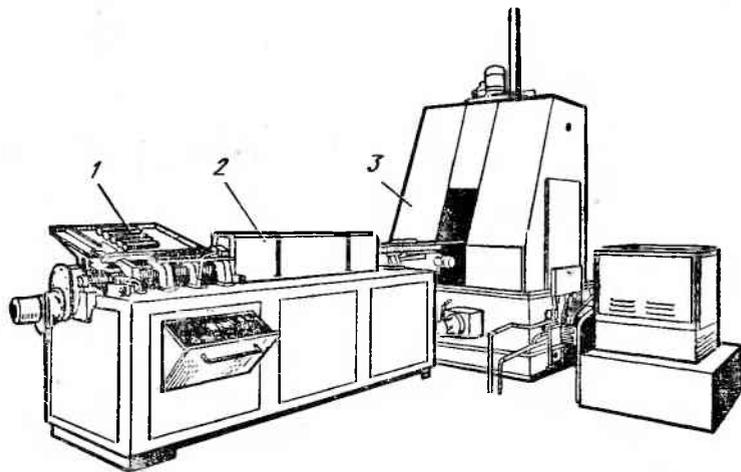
Радиально-ковочная машина с индукционной нагревательной установкой: 1 — подающее устройство, 2 — нагревательная установка, 3 — радиально-ковочная машина
